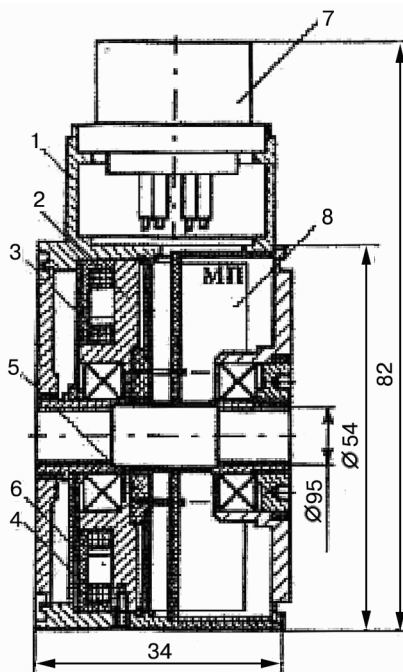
Конструктивная схема датчика угловых перемещений
